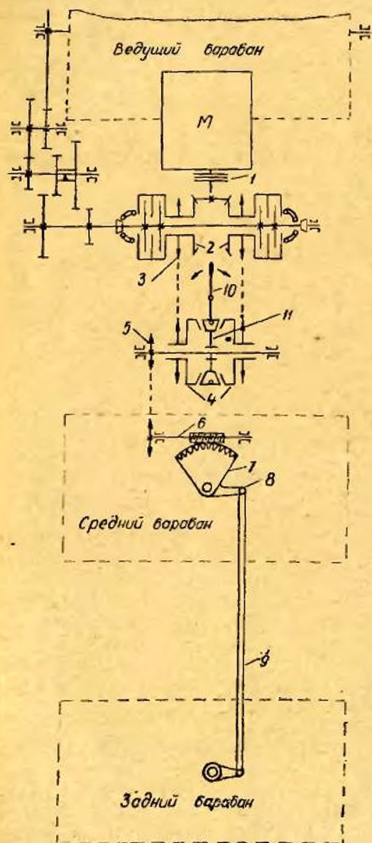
Кинематическая схема и схема рулевого управления катка триплекс
